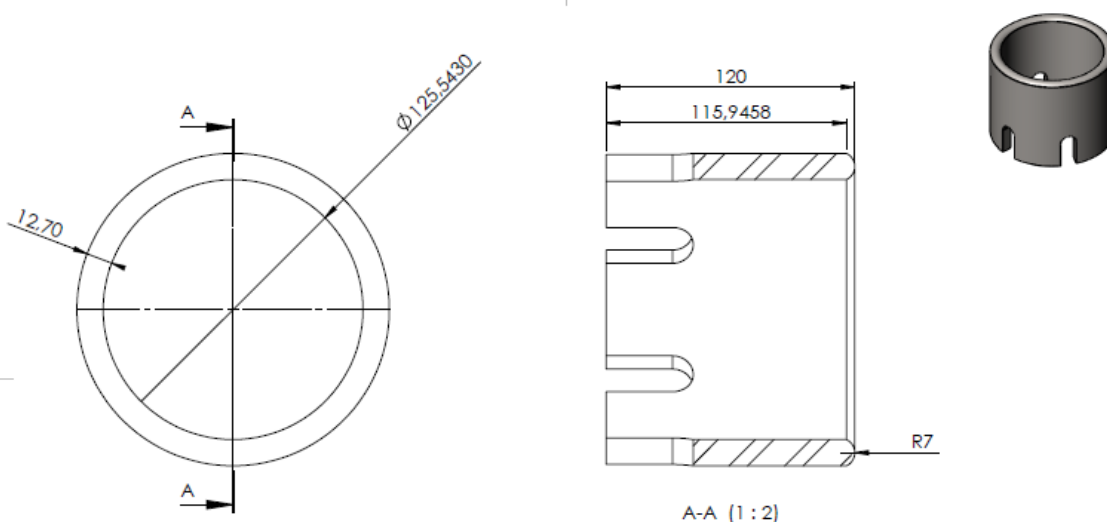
Desenho e dimensões em milímetros do tubo utilizado.
